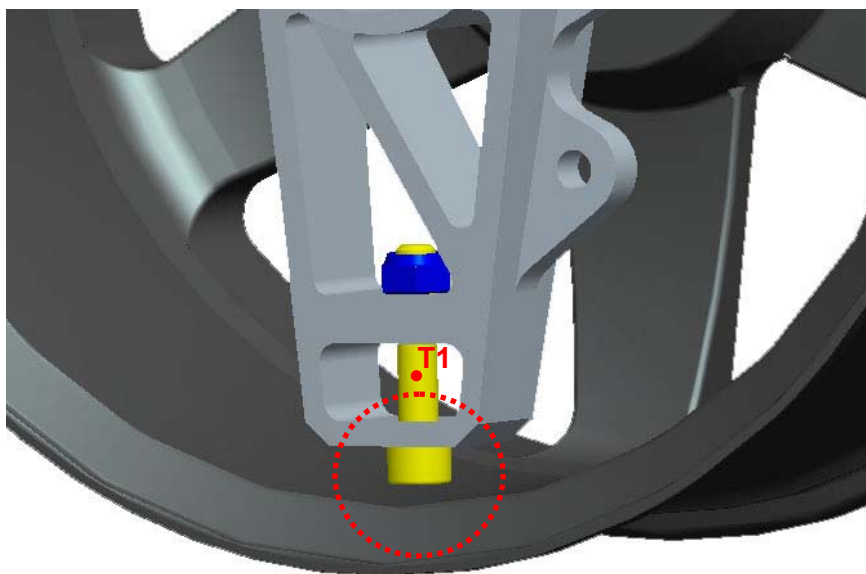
Geometrie hlavních souřadnic přední těhlice
